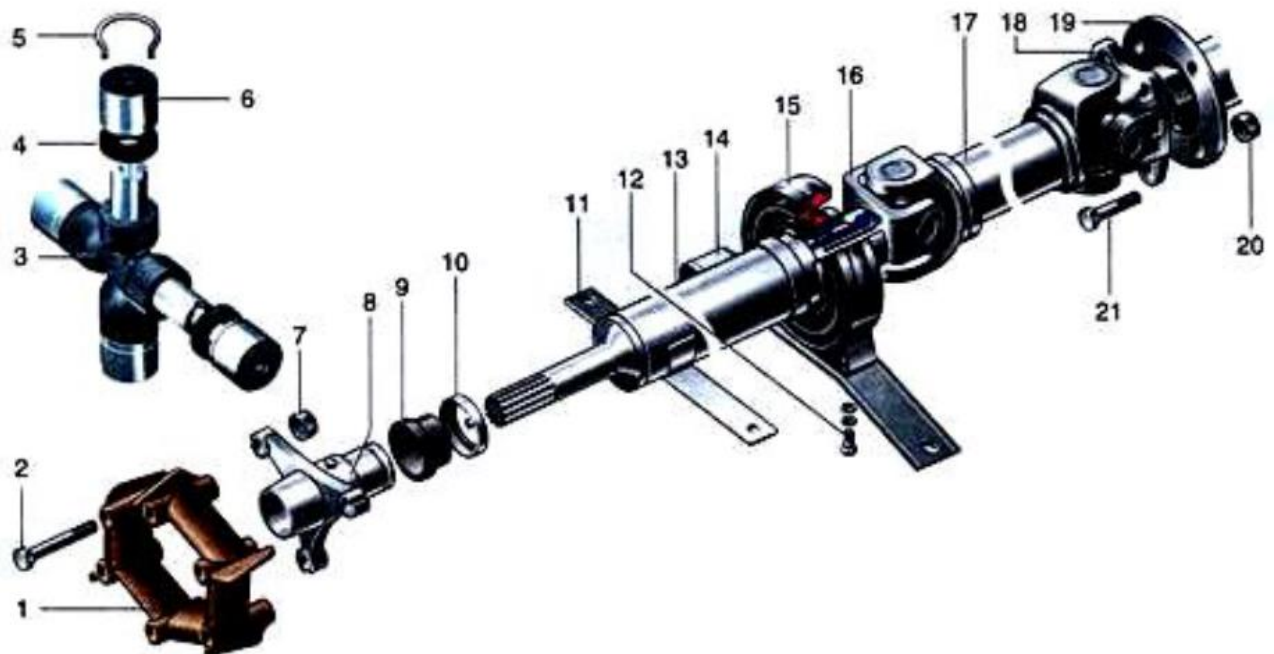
Загальний вигляд карданного валу: 1 – вилка фланець; 2 – підшипник; 3 – кільце для герметичності; 4 – хрестовик; 5 – вилка; 6 – гайка; 7 – гайка, 9 – гайка, 11 – шайба
